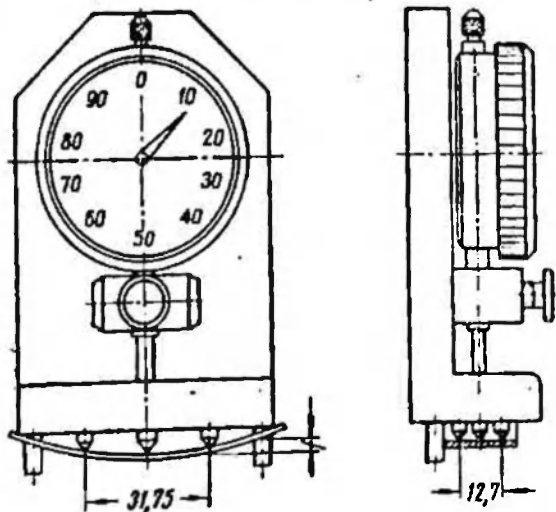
Приспособление для измерения стрелы прогиба образцов
